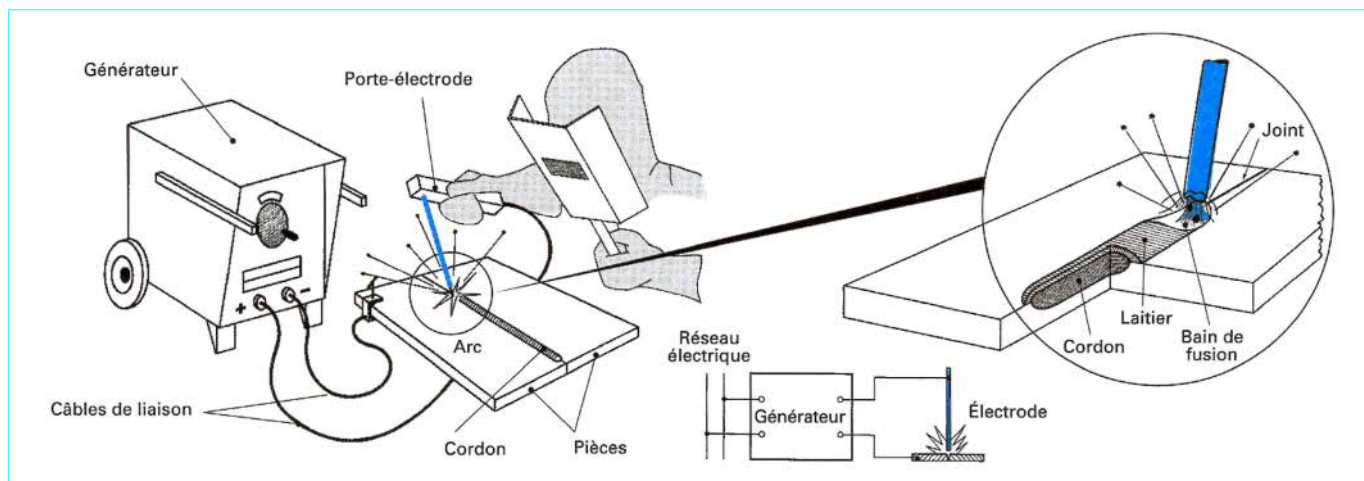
Soudage à l'électrode enrobée : principe
